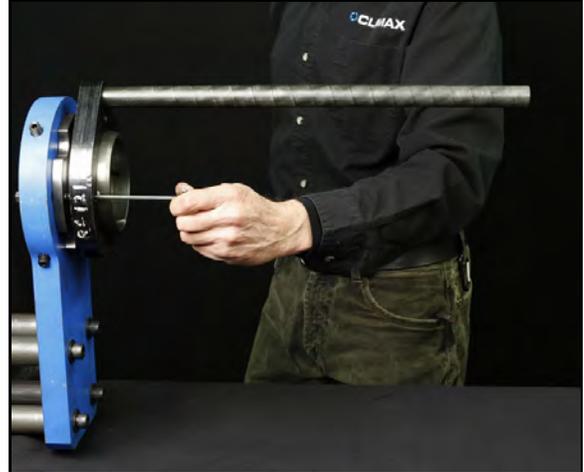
SERRAGE DES VIS DE RÉGLAGE
